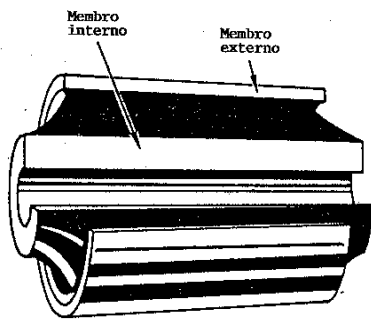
Bucha de borracha, no formato de tubo, para fixação de motor.
